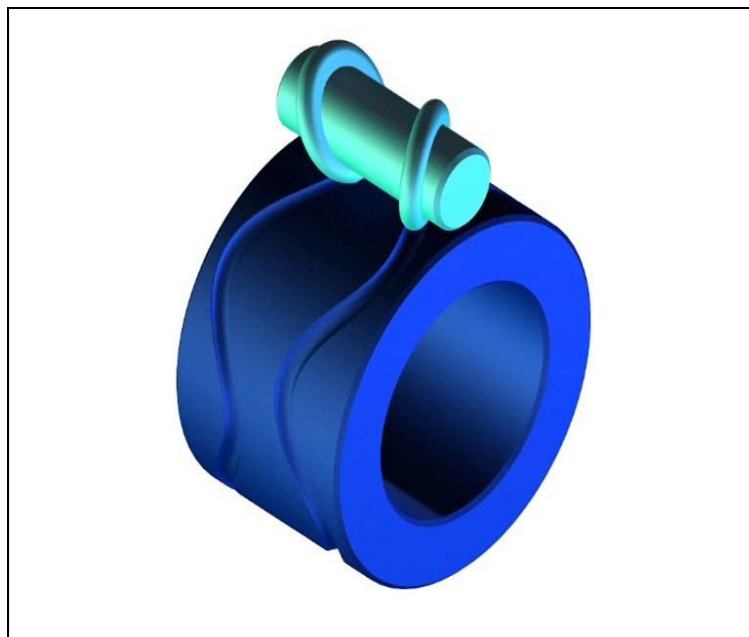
Общий вид виткового механизма с дорожками качения на цилиндре
